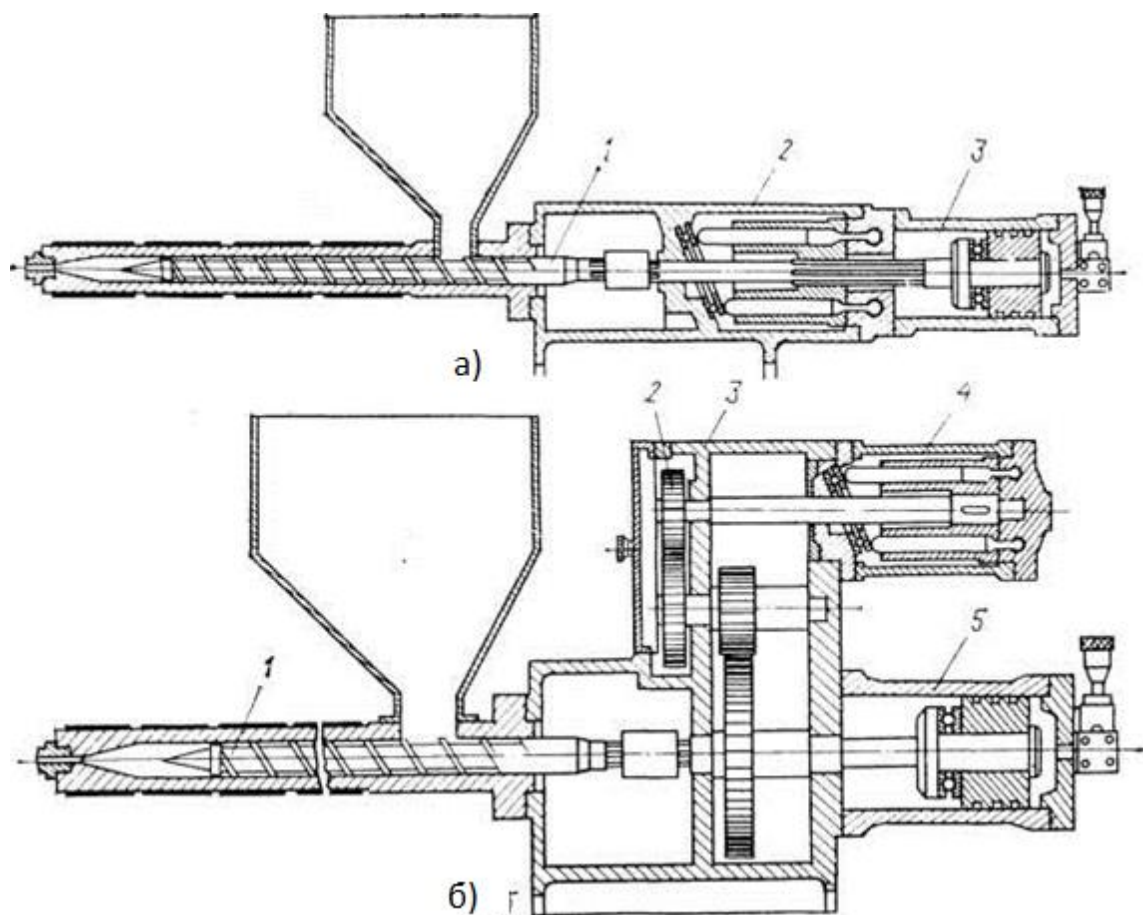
Схеми приводів черв'яка з використанням гідродвигуна приводу для обертання:
